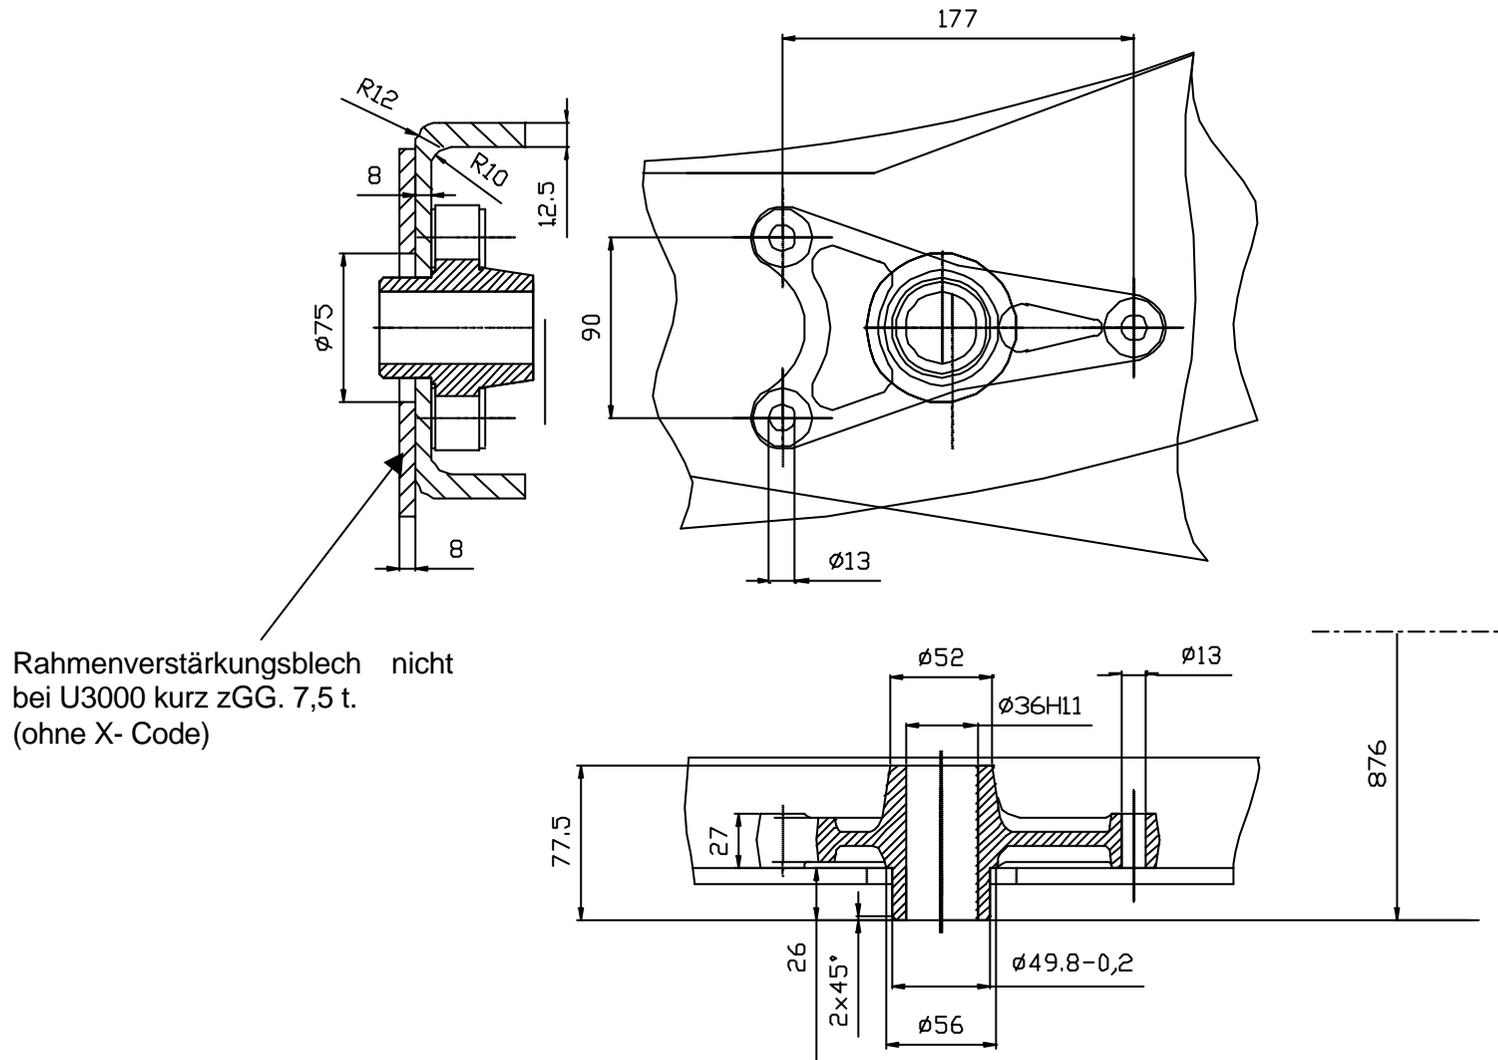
Anbaubock Mitte Teile-Nummer: A 437 551 00 21, Gerätebefestigung über Bolzen Æ 36 mm
